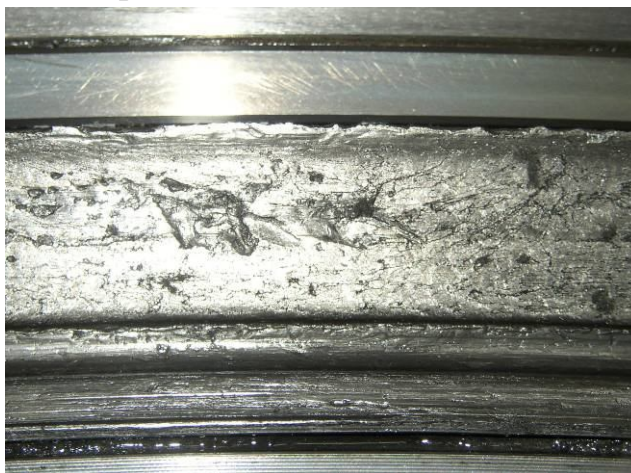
Усталостные трещины поверхностного слоя беговой дорожки подшипника
